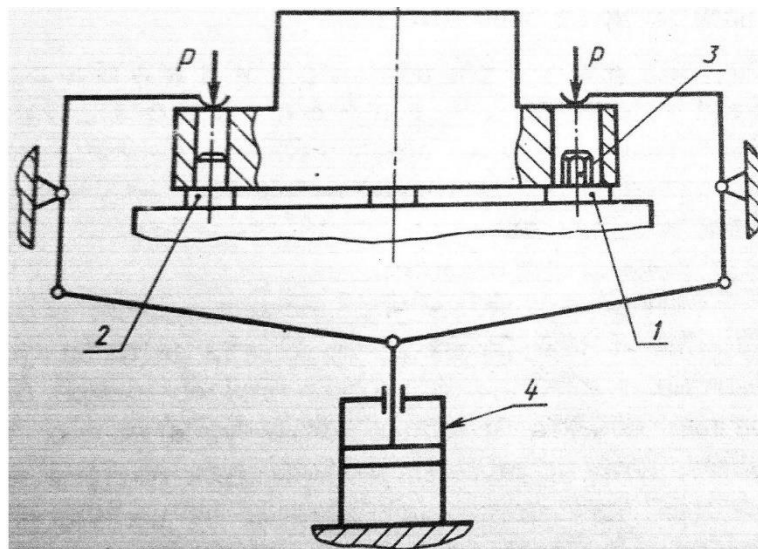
Принципиальная схема приспособления для установки заготовок корпусного типа
